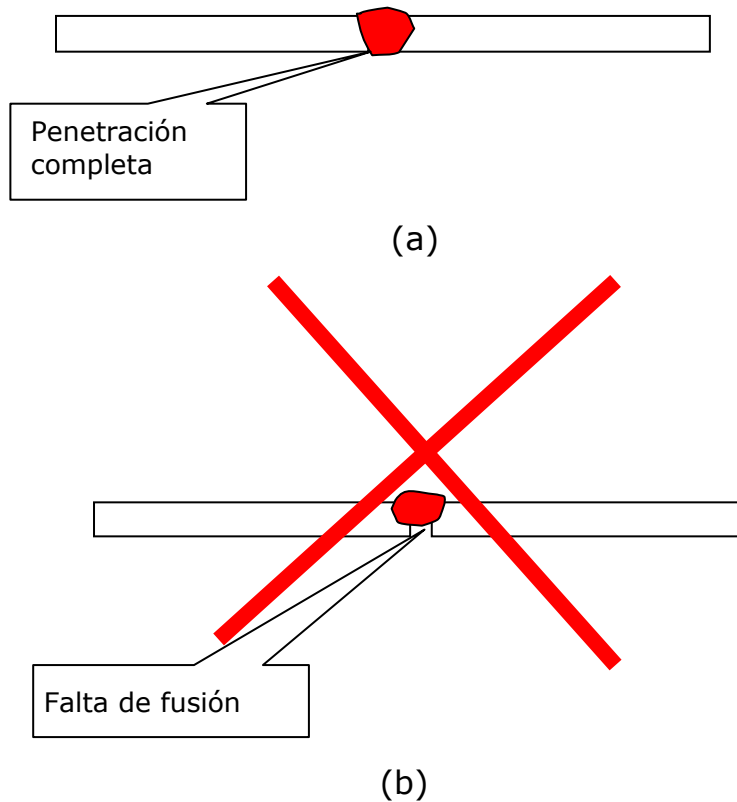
(a) Penetración completa, (b) Falta de penetración.
